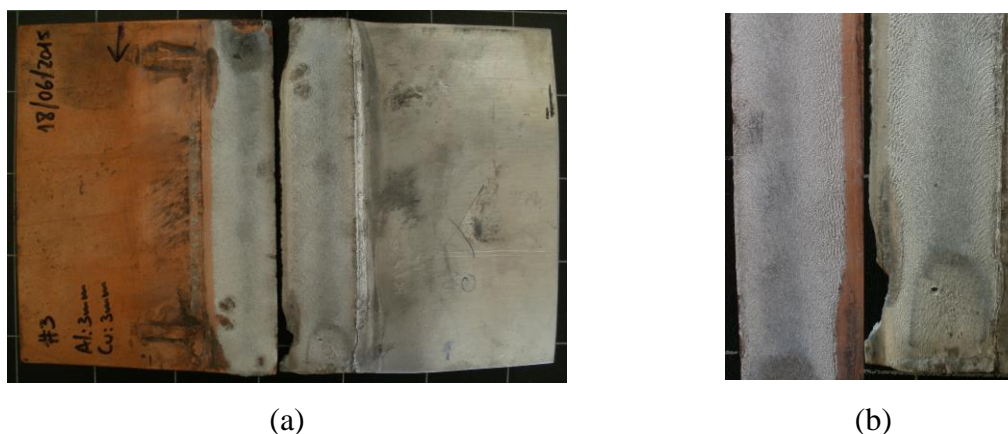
(a) Soldadura UEW2; (b) Detalhe da zona soldada.
